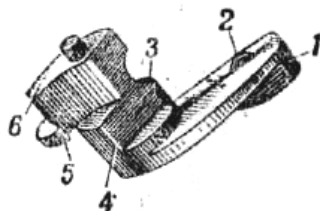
Предохранитель: 1 – флажок предохранителя; 2 – фиксатор; 3 – уступ; 4 – ребро; 5 – зацеп; 6 – выступ
